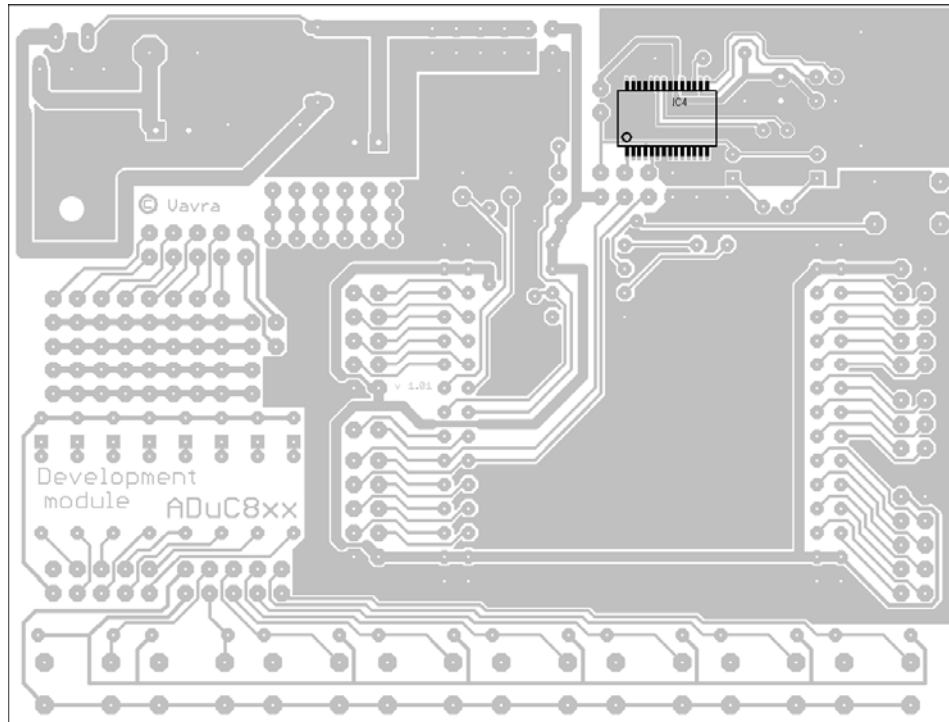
Rozmístění součástek zadní strany plošného spoje
